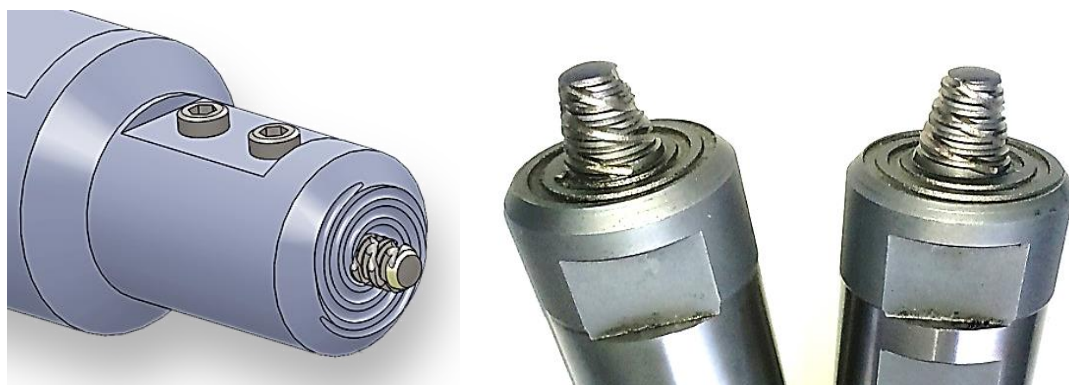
Проекты прогрессивного инструмента: 3D модель и готовые изделия
